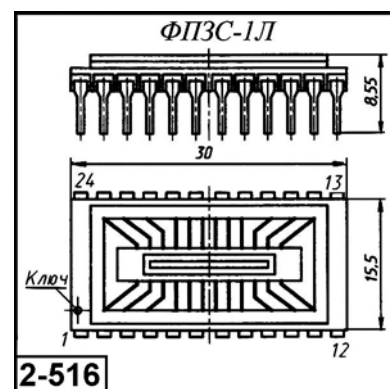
Внешний вид и габаритные размеры ФПЗС1Л и ФПЗС1Л-1
